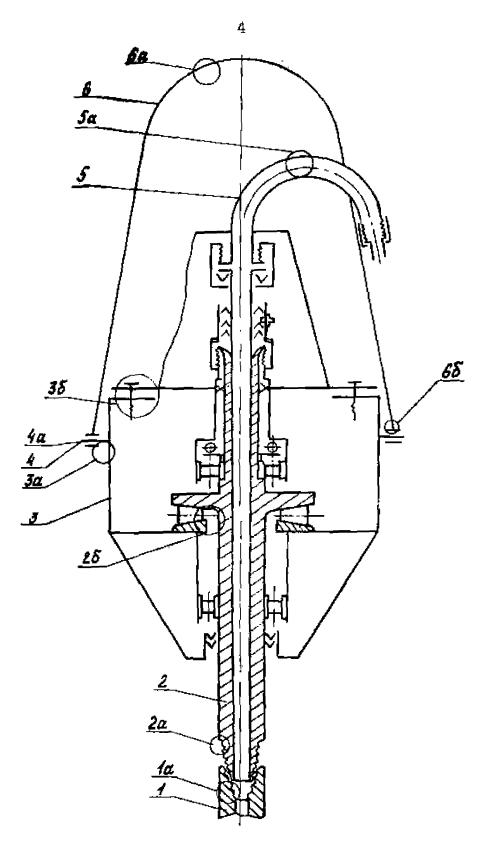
Зоны контроля вертлюга; 1 - переводник; 2 - ствол; 3 - корпус; 4 - пальцы; 5 - труба напорная (отвод); 6 - штроп
